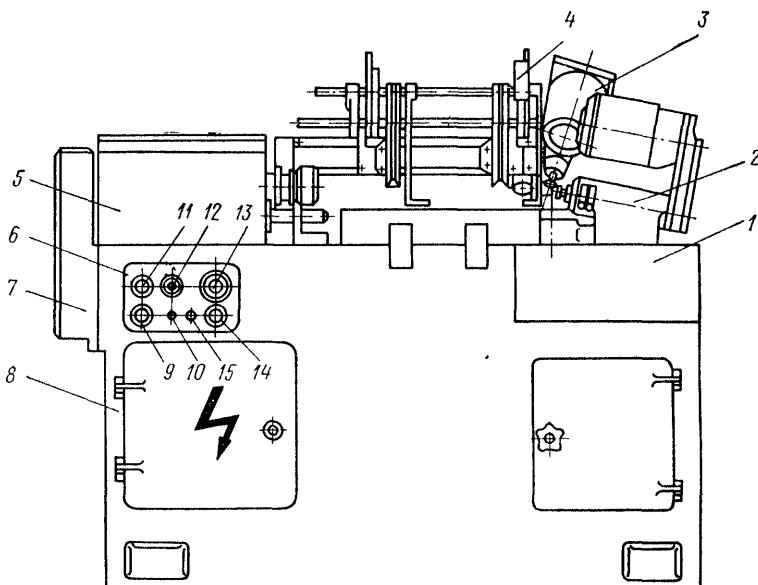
Специальный сверлофрезерный автомат модели СИ-031:
